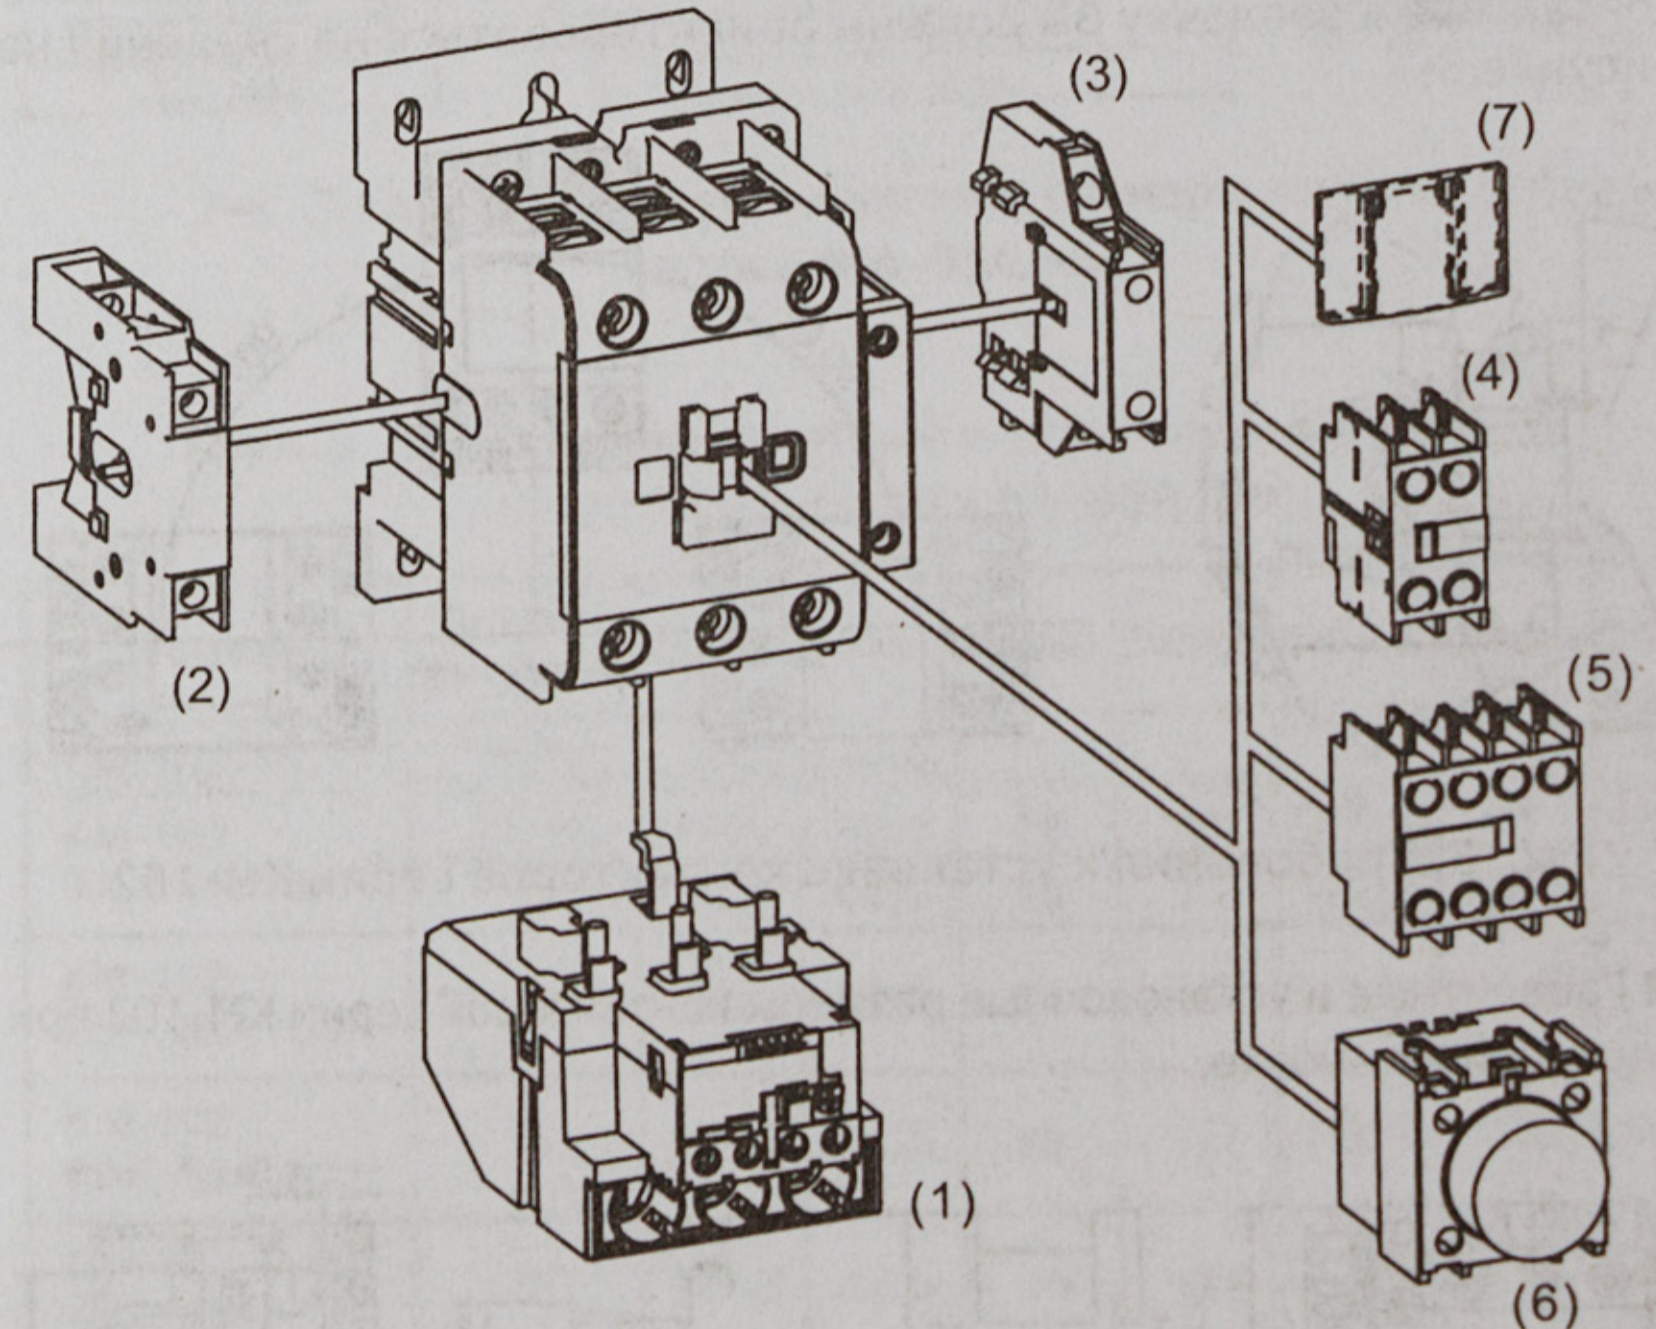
Контактор КМ-102 и схематическая установка аксессуаров
